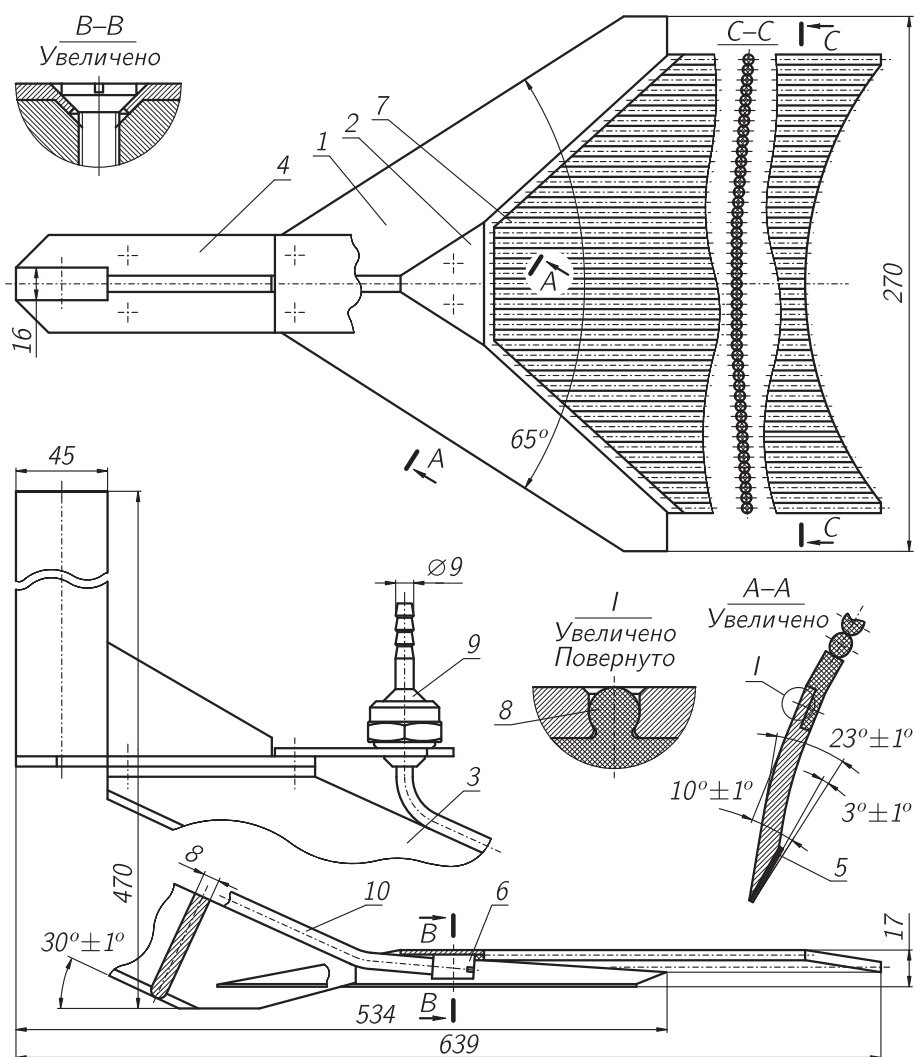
Разработанный рабочий орган для внутрпочвенного внесения гербицидов на комковатых почвах: 1 — лемехи; 2 — сводообразующая часть; 3 и 4 — наклонная и вертикальная части стойки; 5 — наплавленный слой; 6 — распылитель; 7 — прутковый козырек; 8 — фиксатор козырька; 9 — фильтр-клапан-отсекатель; 10 — канал для подвода рабочей жидкости
